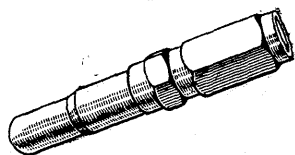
Приспособление для развальцовки труб с помощью пуансона-расширителя.
